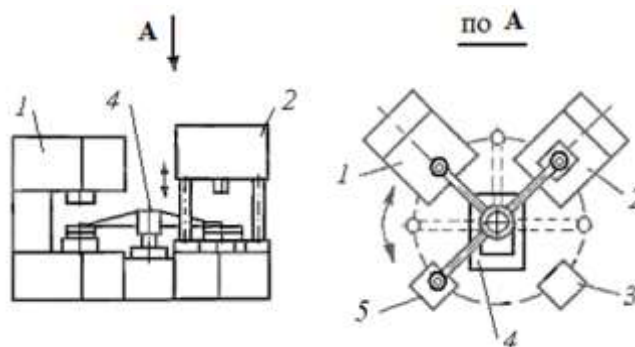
Схема обслуживания ПР двух консольных прессов холодной штамповки деталей: 1–консольный пресс; 2 – двухстоечный пресс; 3 – магазин деталей; 4– трехрукий ПР; 5 –магазин заготовок
